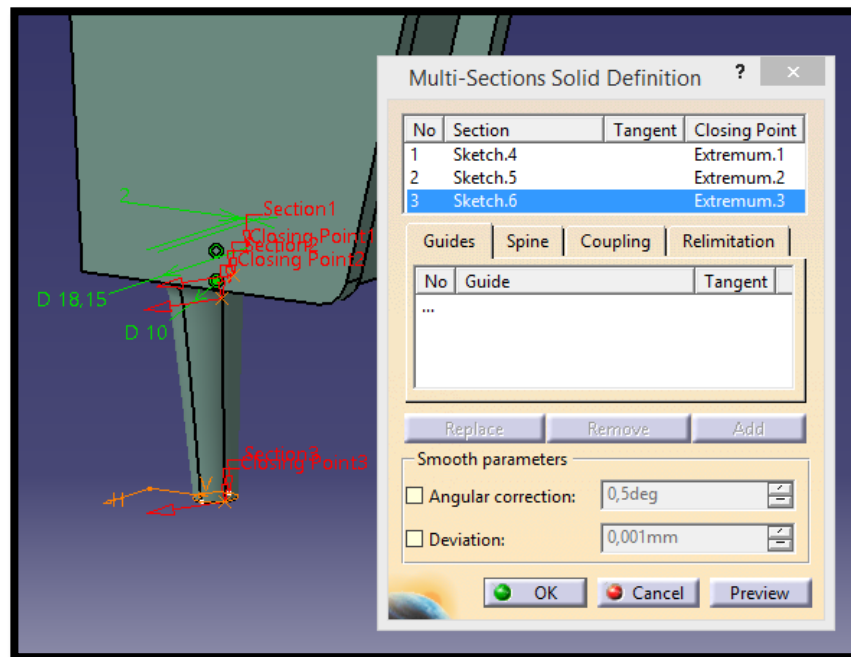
Seat mounting frame 11: Multi-sections Solid parte principal
